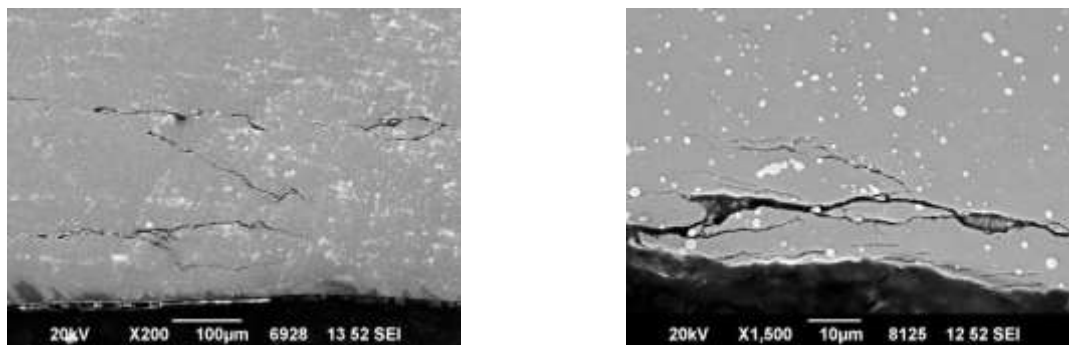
Подповерхностные трещины, развивающиеся от дорожек качения наружных колец подшипников №№ 1 и 2
